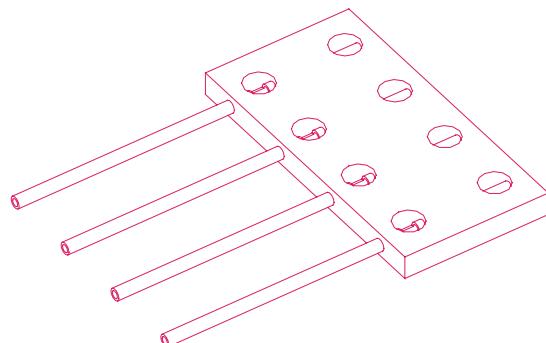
El elemento más simple posible, con una sola protección, seccionado para poder apreciar la configuración interior.
